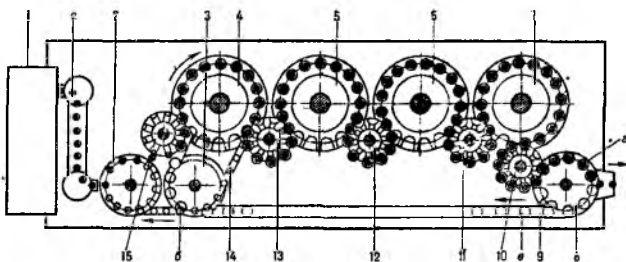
Схема роторно-конвейерной линии для литья термопластов под давлением: а – заготовки; б – инжекц. цилиндр; в – пресс-форма; г – изделия; 1 – бункер; 2 – ротор дозирования; 3 – ротор смыкания пресс-форм; 4 – ротор инжекции; 5, 6 – роторы охлаждения; 7 – ротор размыкания пресс-форм; 8 – ротор съема изделий; 9, 14 – конвейеры возврата пресс-форм и инжекц. цилиндров; 10–13, 15 – транспортные роторы.
